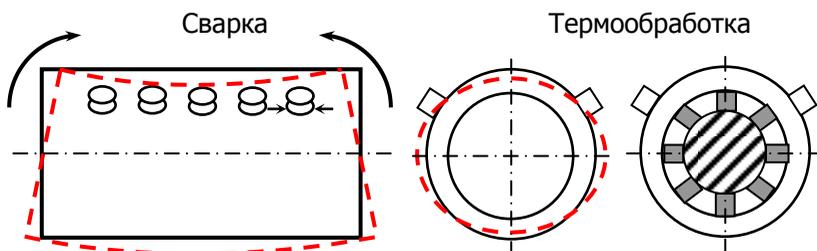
Искривление торца обечайки в результате сварки асимметрично расположенных патрубков и схема предотвращения сварочных деформаций.
